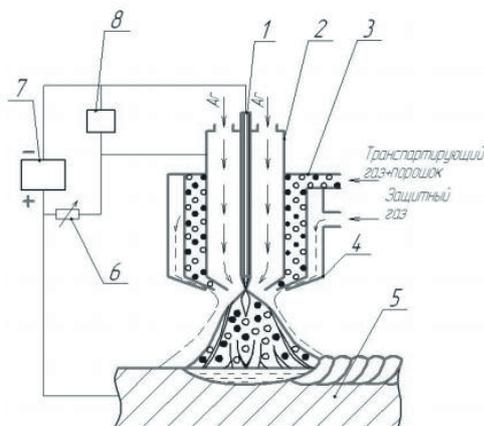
Схема плазменно-порошковой наплавки: 1 – электрод; 2 – плазменное сопло; 3 – фокусирующее сопло; 4 – защитное сопло; 5 – изделие; 6 – балластный реостат; 7 – источник питания; 8 – осциллятор
